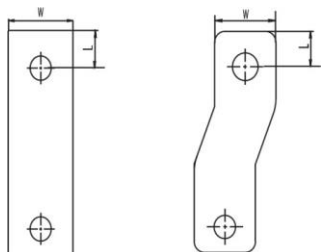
Габаритные и установочные размеры ручки на дверь шкафа РП-330, мм
